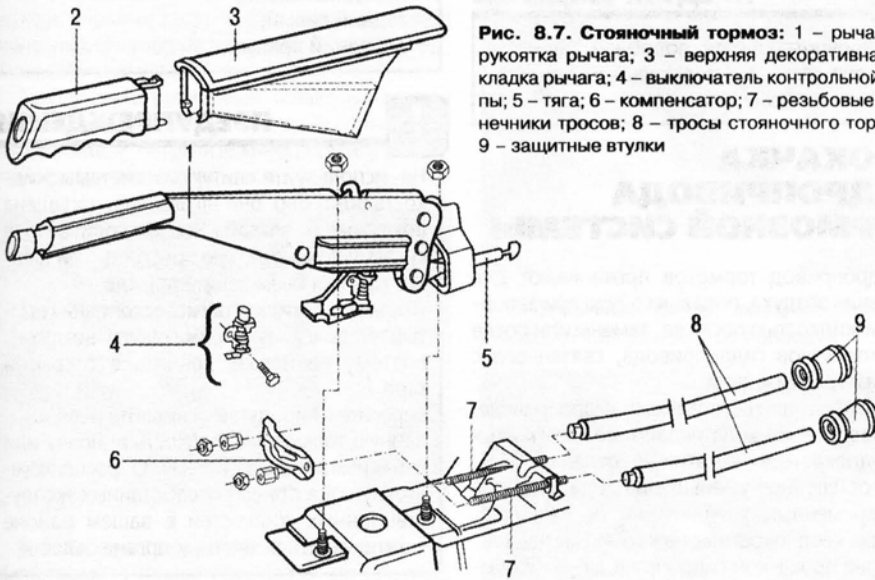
Стояночный тормоз: 1 – рычаг; 2 – рукоятка рычага; 3 – верхняя декоративная накладка рычага; 4 – выключатель контрольной лампы; 5 – тяга; 6 – компенсатор; 7 – резьбовые наконечники тросов; 8 – тросы стояночного тормоза; 9 – защитные втулки
